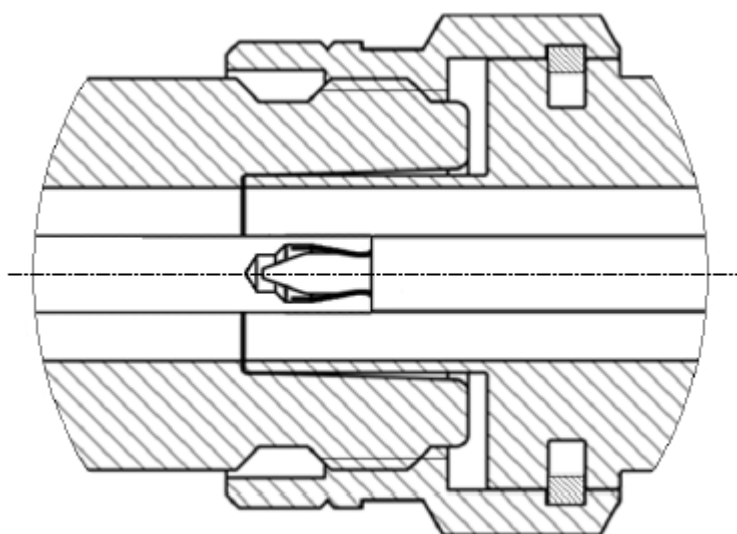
Соединители тип N (розетка слева, вилка справа)
